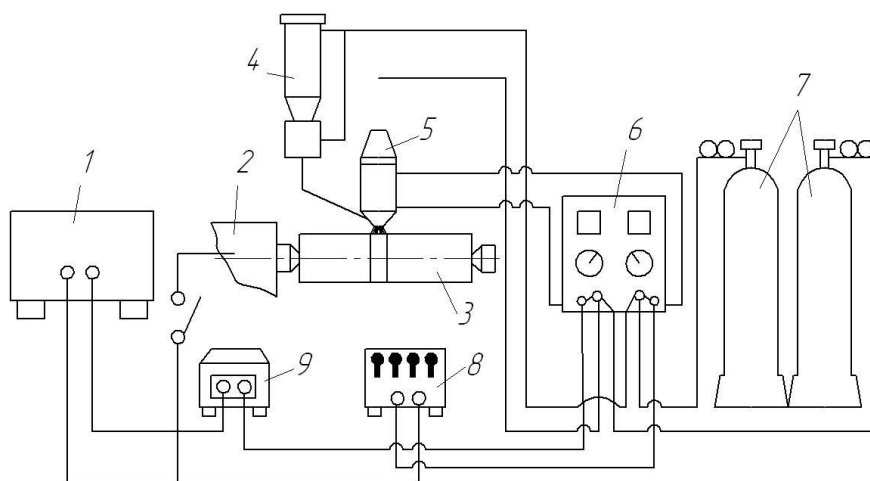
Схема плазменной наплавки двумя присадочными проволоками
